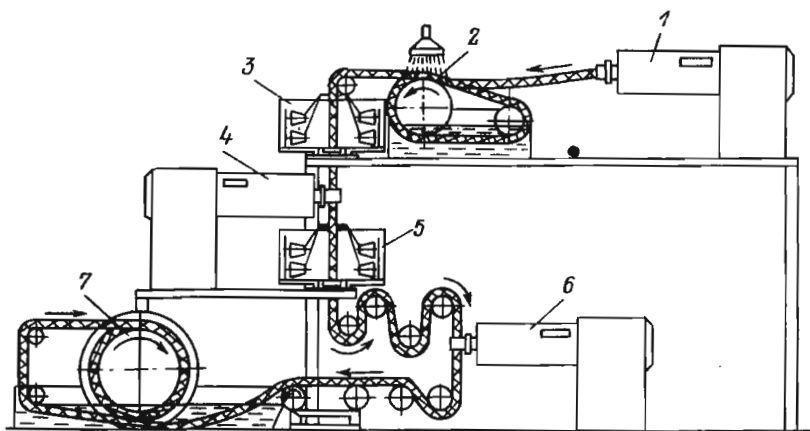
Схема линии НВАНР для сборки рукавов навивочной конструкции бездорновым способом:
